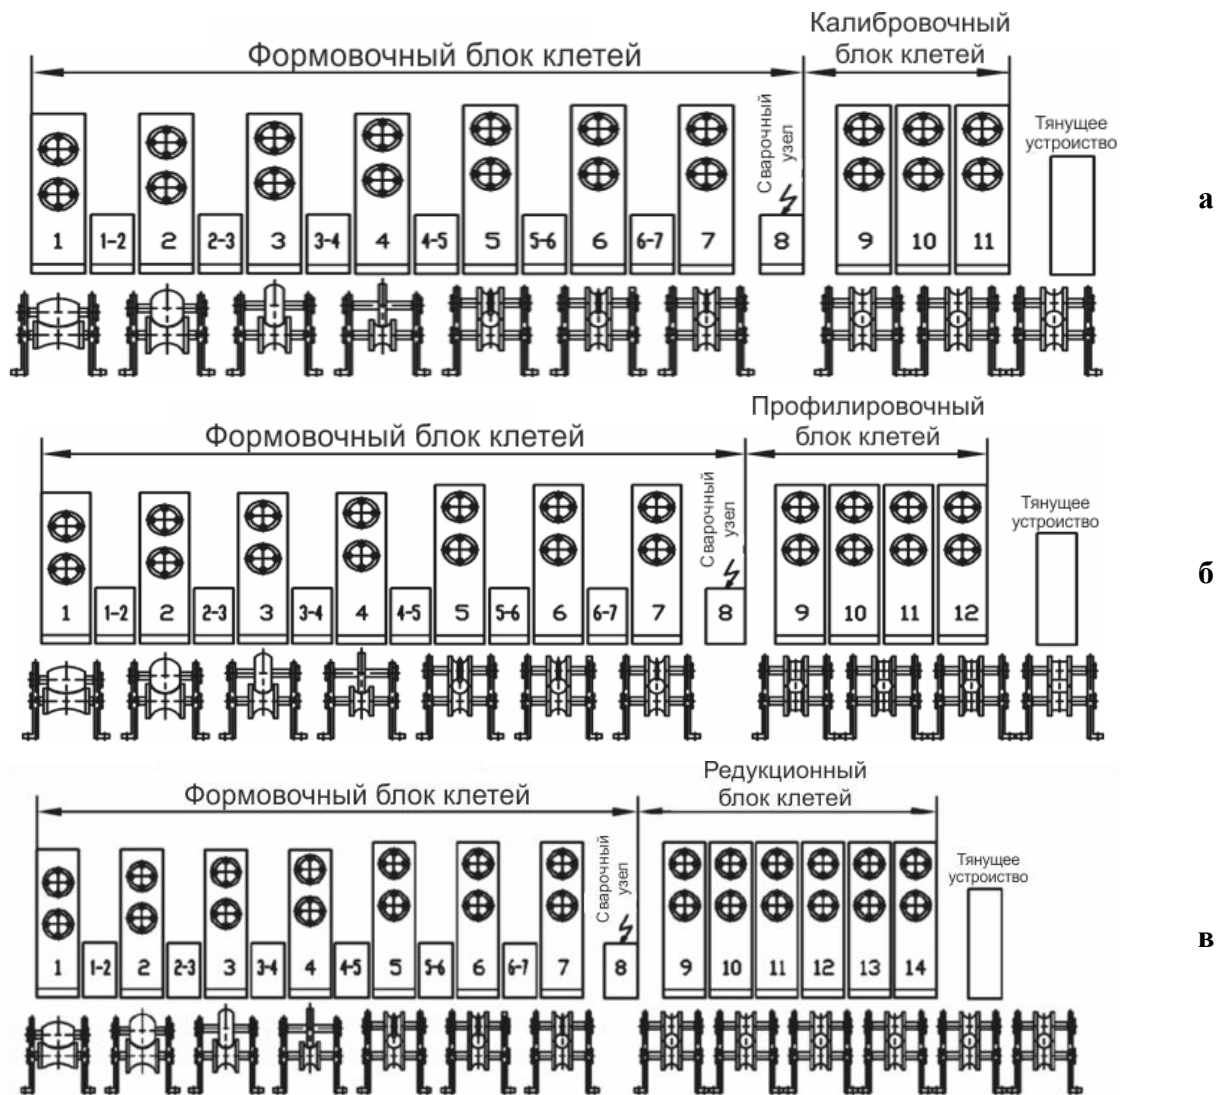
Основные производственные компоновки: а) компоновка клеток для получения сварных труб круглого сечения; б) компоновка клеток для получения сварных профилированных труб из круглой заготовки; в) компоновка клеток для получения сварных холодно-редуцированных труб
